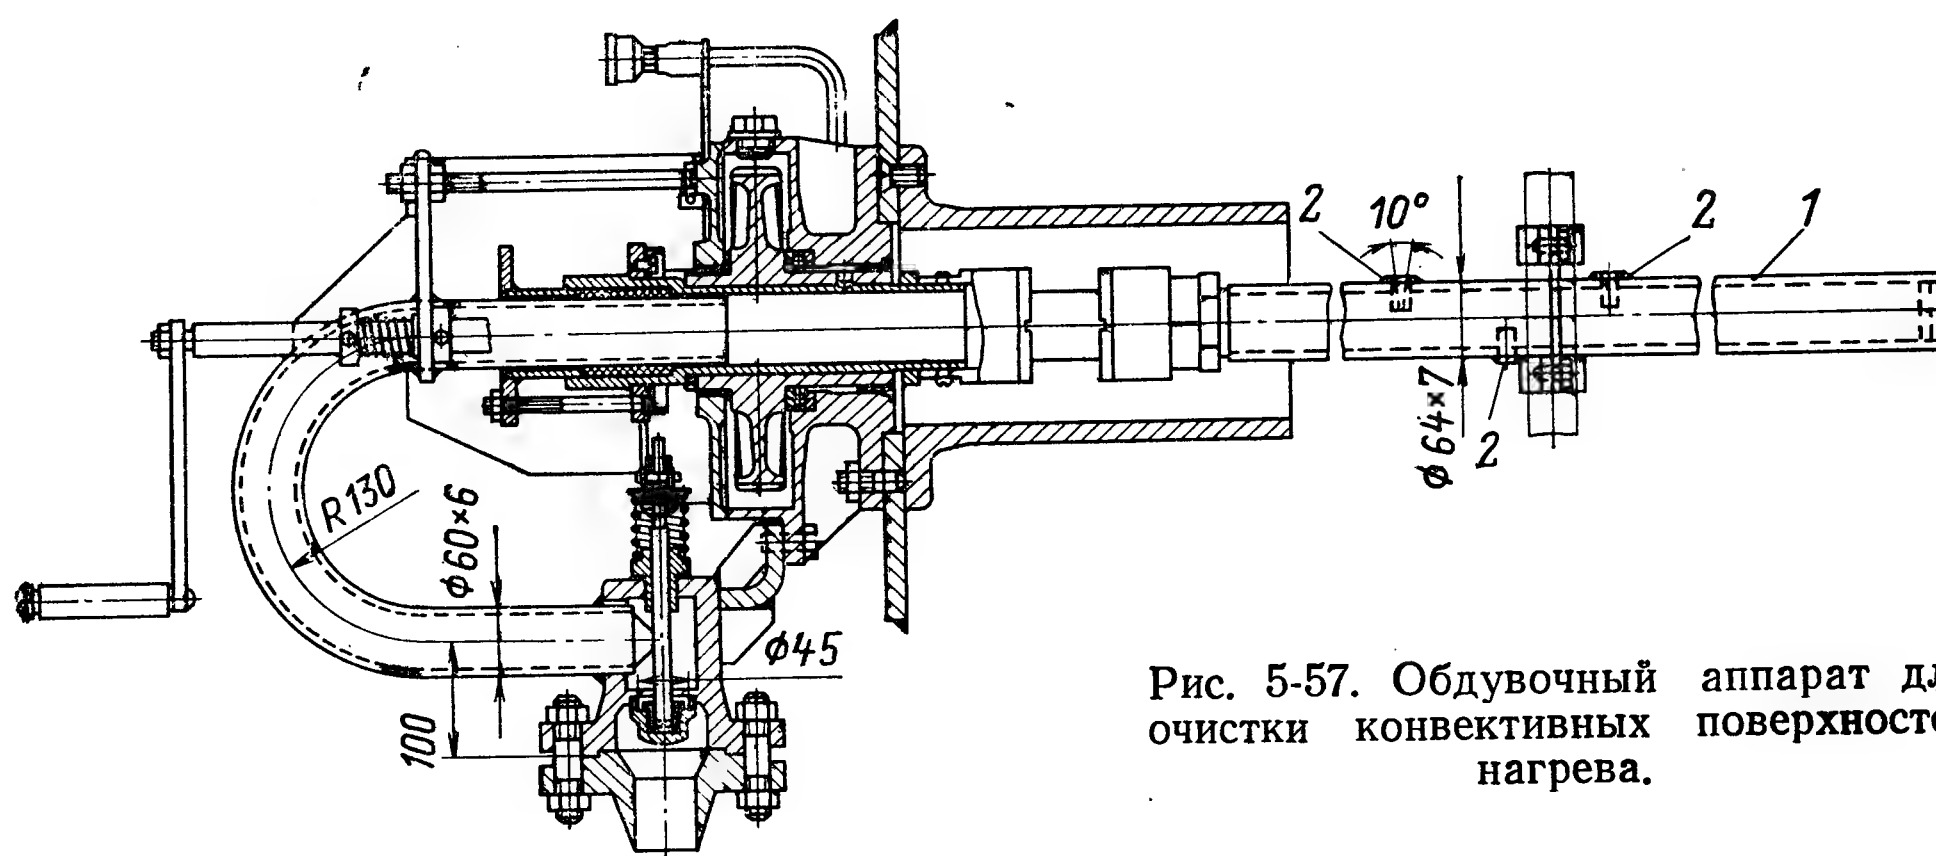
Обдувочный аппарат для очистки конвективных поверхностей нагрева.
